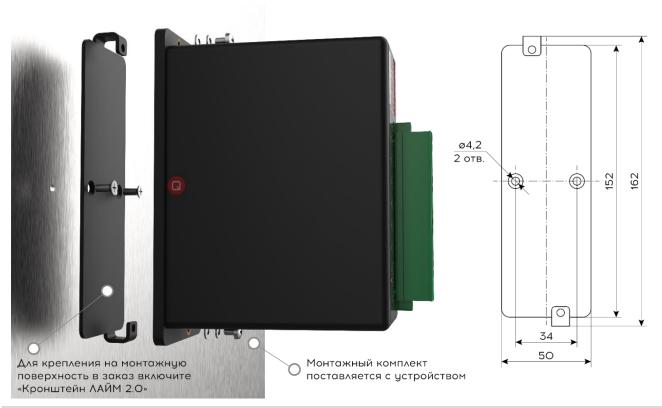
Установочные размеры на монтажную поверхность
